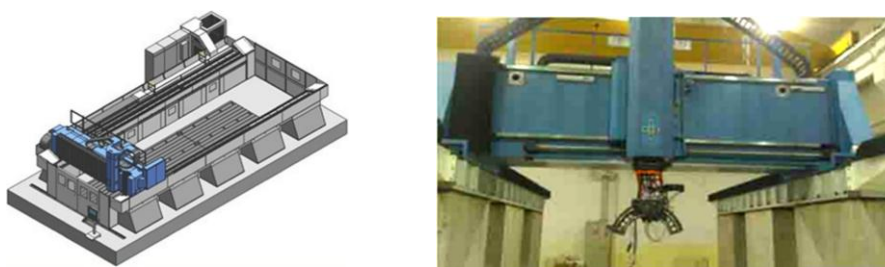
Система двусторонней лазерной сварки [17]
